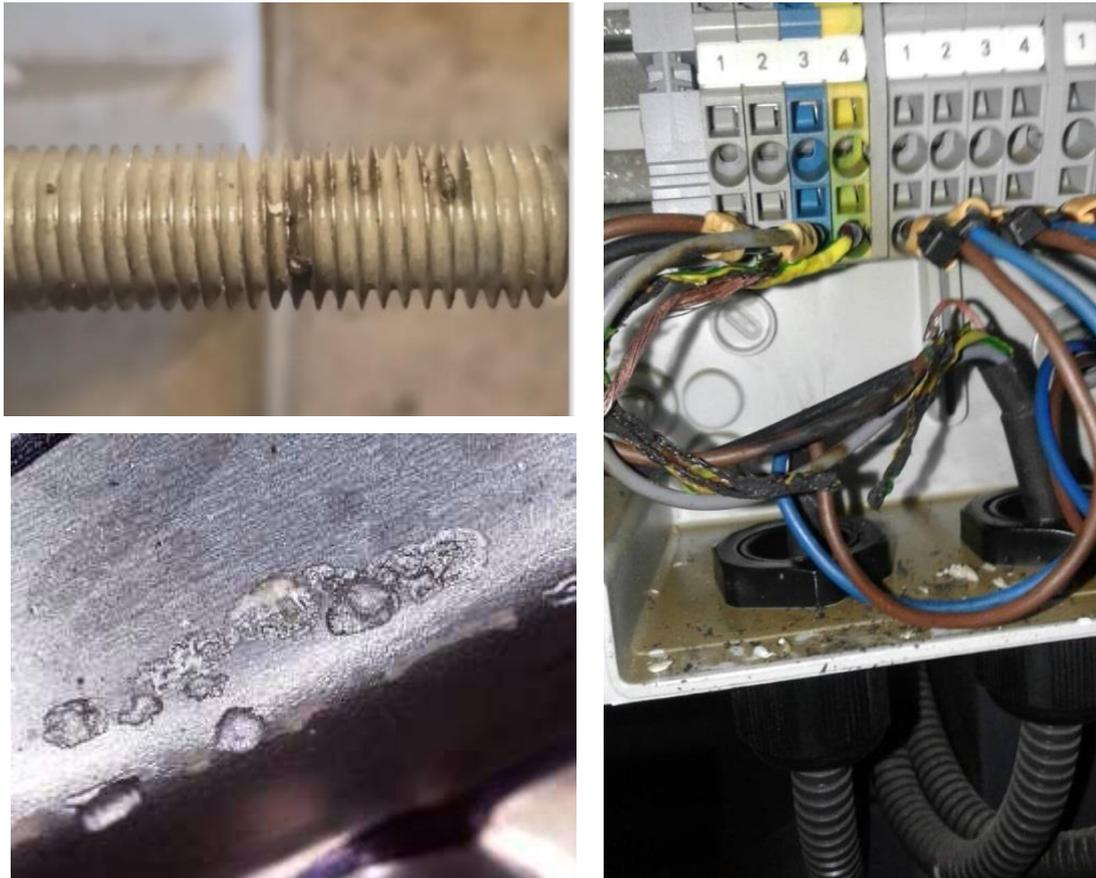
Последствия неправильного подключения «массы» сварочного аппарата
